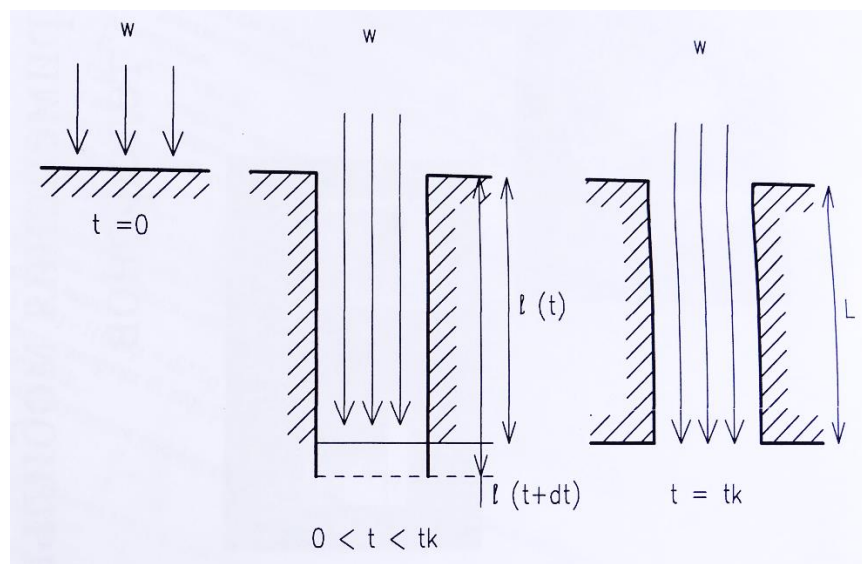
Початкова, проміжна і кінцева стадії свердління металу лазером
